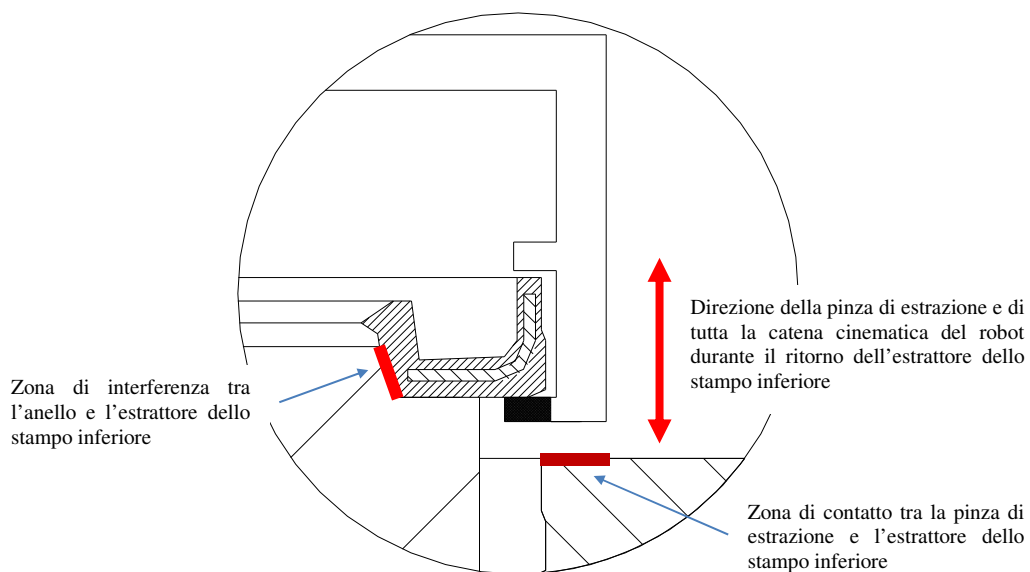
Particolare della fase di estrazione anello dallo stampo.
